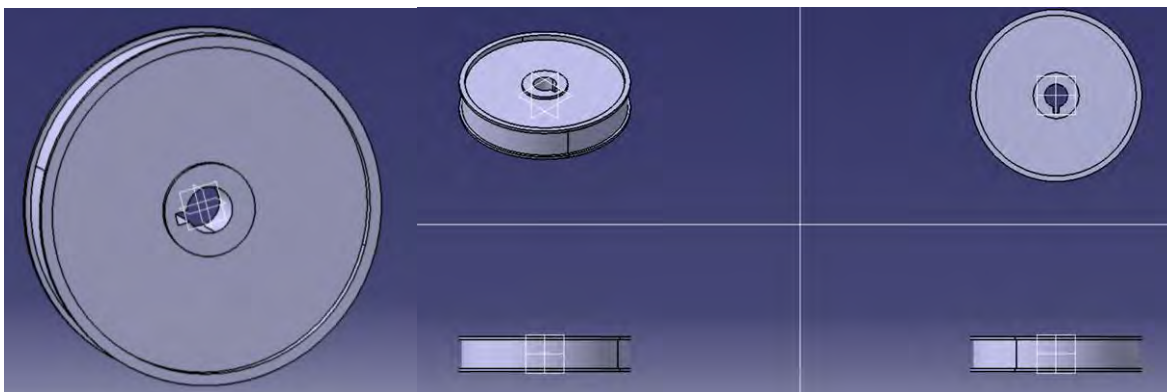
Vistas del dibujo mecánico de rodete compresor dinámico (realizado en Catia V5)
